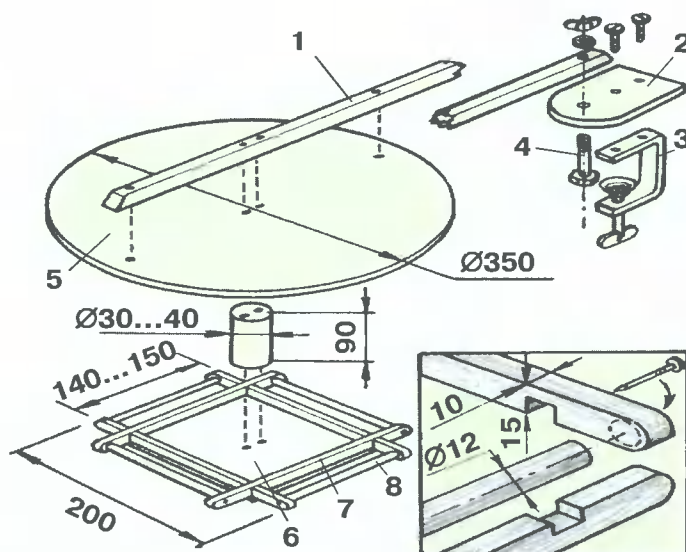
Детали кормушки: 1 — штанга; 2 — пластина; 3 — струбина; 4 — поворотная ось; 5 — экран; 6 — дно; 7 — бортик; 8 — насест.
